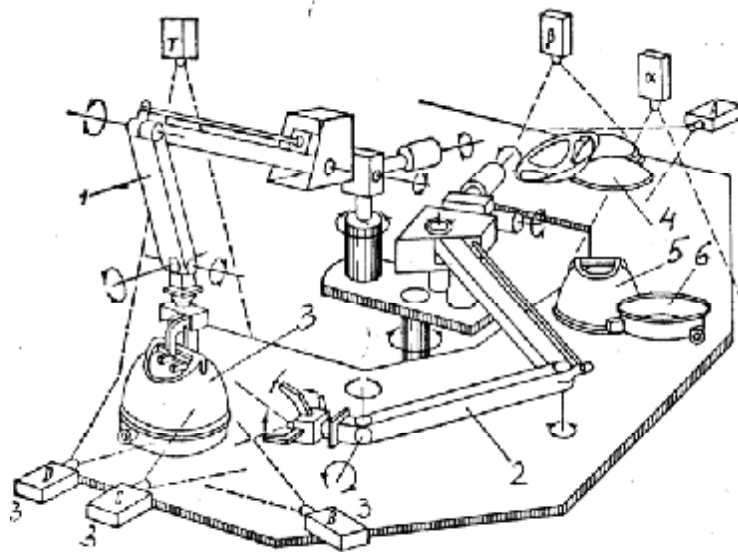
Робототехнический комплекс для сборки пылесосов.
